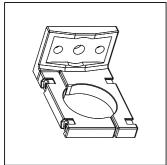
LE COLLIER EN ÉQUERRE (REF. YXW-0001-000)
